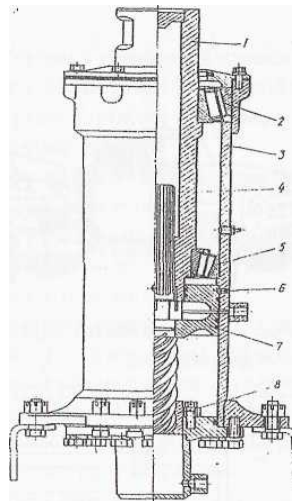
Механізм повороту крану : 1 — стійка; 2, 5 — конічні підшипники; 3 — корпус; 4 — гвинт; б — корпус кришки; 7 — поршень; 8 — гайка
